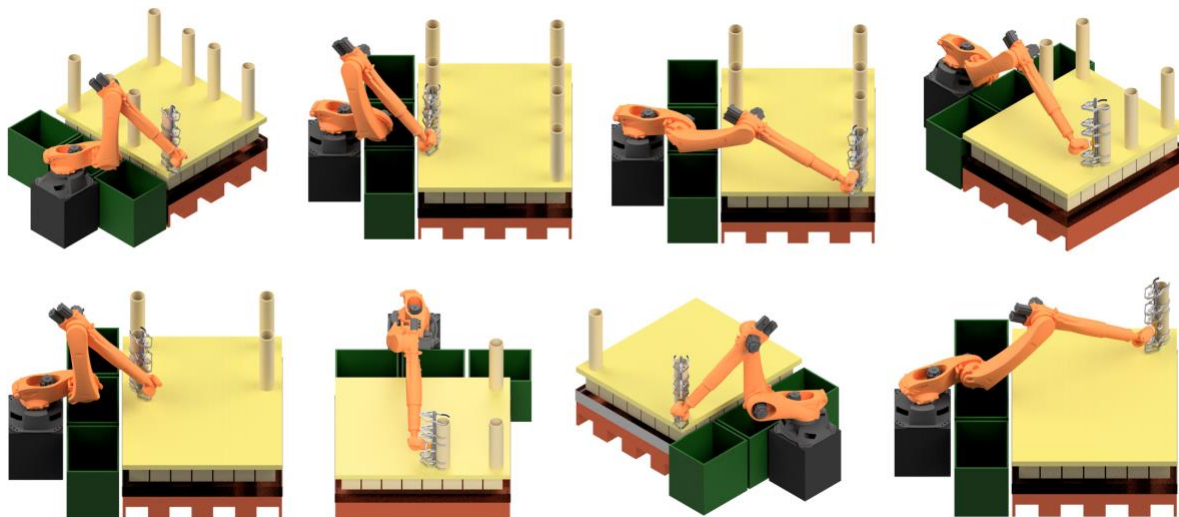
Pracovní zóna robota KUKA KR 120 R3900 Ultra K [31]
